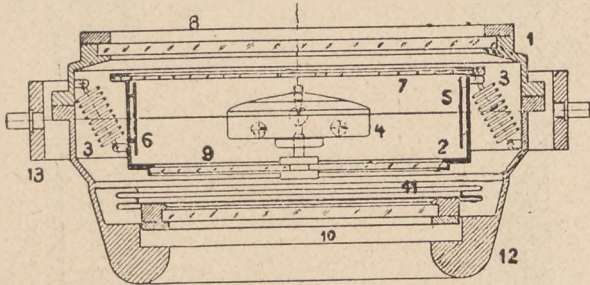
Motorschiffskompaß von Plath. 1 Äußerer Kompaßkessel, 2 innerer Kompaßkessel, 3 Aufhängefedern des Innentessels, 4 Schwimmer, 5 Kompaßrose, 6 Steuerstrich, 7 Glasdeckel des Innentessels, 8 Glasdeckel des Außentessels, 9 Glasboden des Innentessels, 10 Glasboden des Außentessels, 11 Ausdehnungsfalten, 12 Beschwerung des Kessels, 13 Kardanring.
